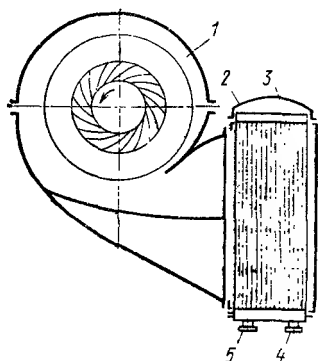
Схема подключения промежуточного холодильника к нижней части корпуса компрессора
